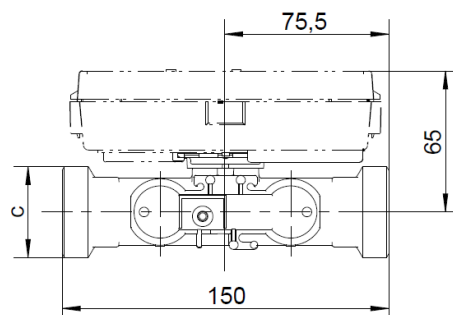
Översikt stora mätares dimensioner - qp 6 med gänga (kort längd face-to-face)
